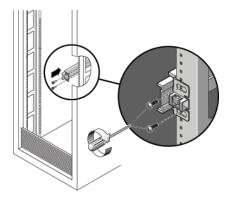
Montage de l'ensemble rail coulissant sur le montant du rack
